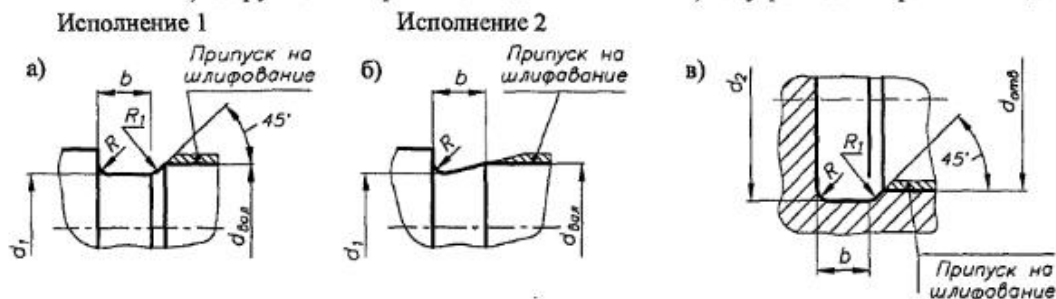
Канавки для выхода шлифовального круга при шлифовании по цилиндру
